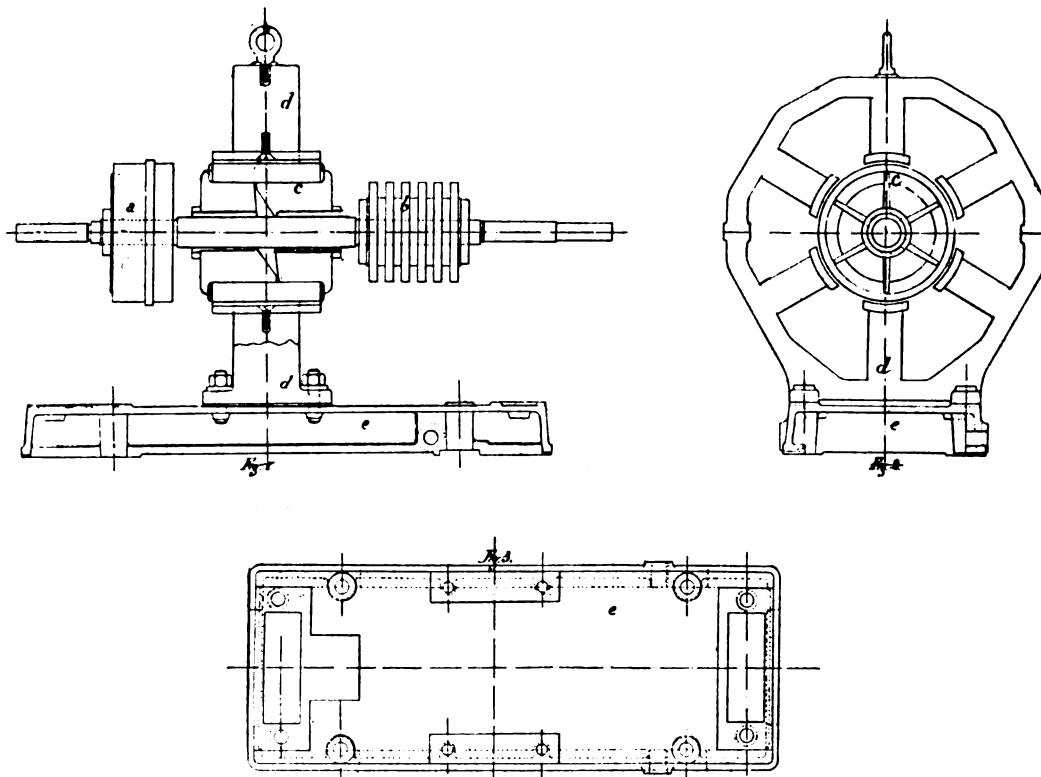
, 2 et 3. — Elévation, coupe transversale et plan du transformateur rotatif Schuckert.
